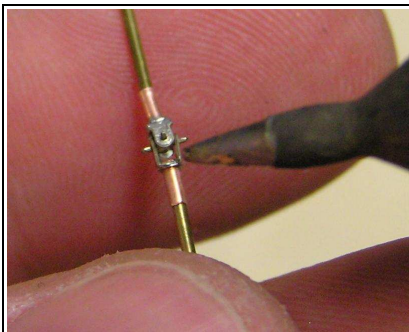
Börtel wieder mit Löffelt bestreichen und mit wenig Zinn verlöten.
